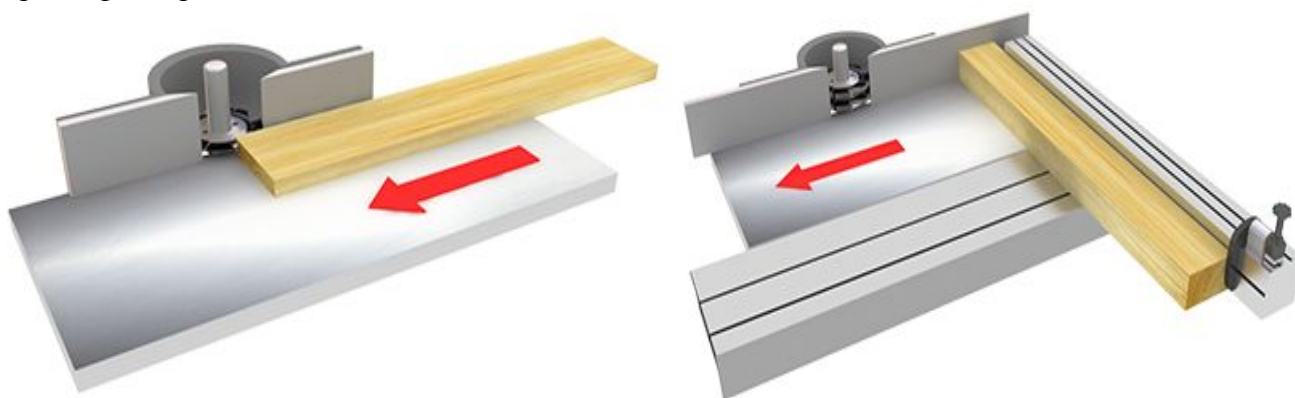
Фрезерування кромки та тоців прямолінійне.
